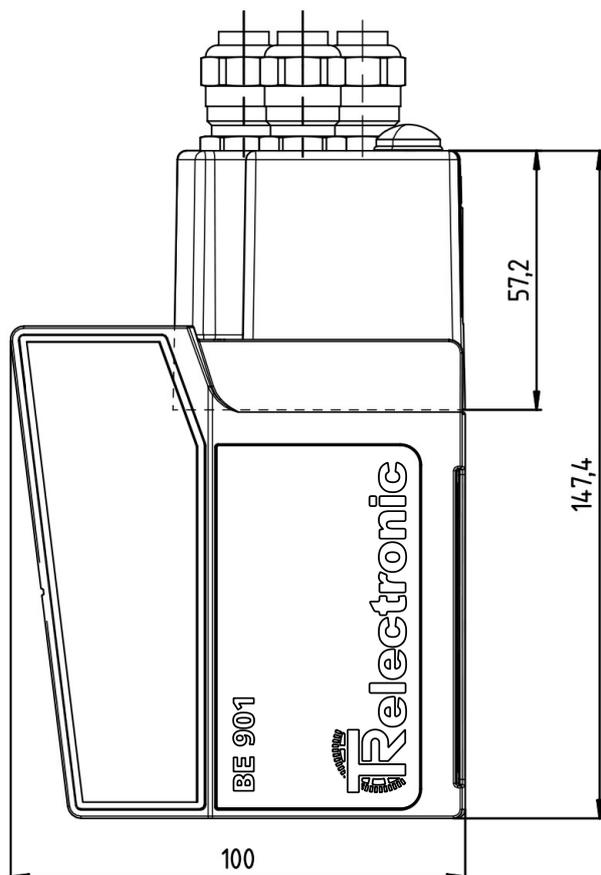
Maßzeichnung BE 901 SSI mit Anschlusshaube BE 901 MK SSI (alle Maße in mm)
